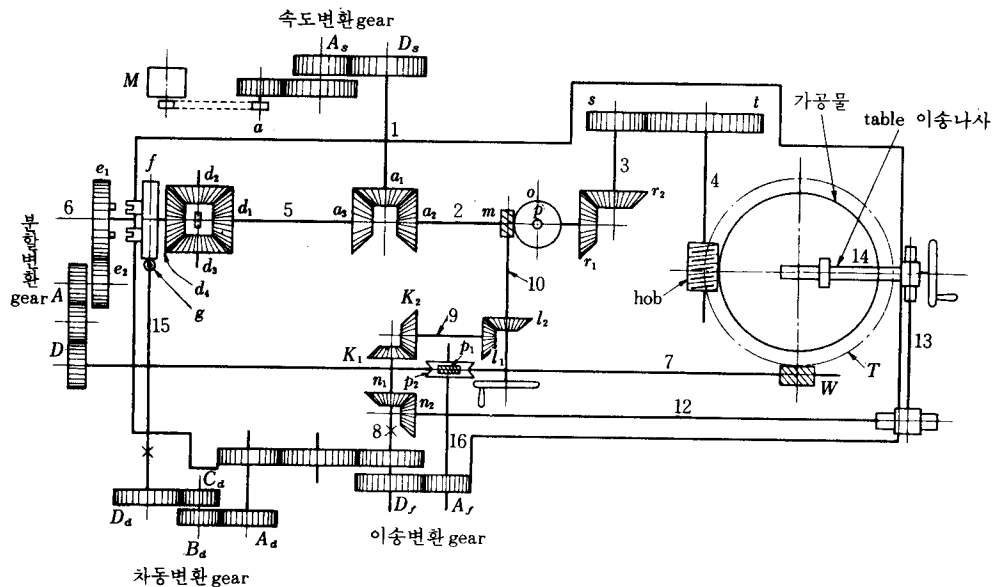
hobbing machine의 驅動系統(平面圖)
